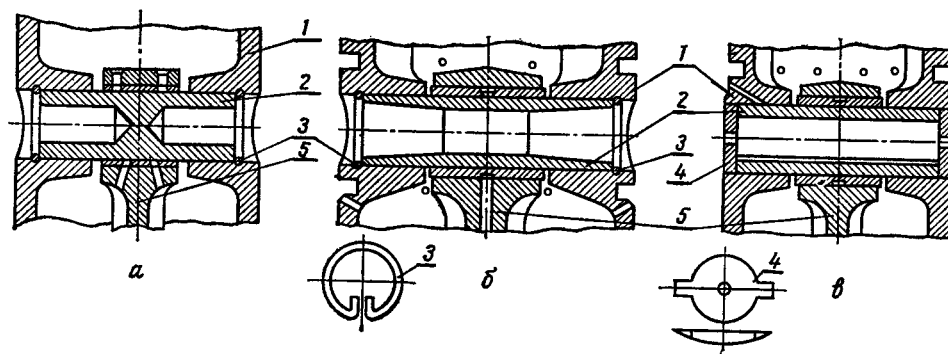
Конструкция поршневых пальцев и способы крепления их от осевых перемещений:
